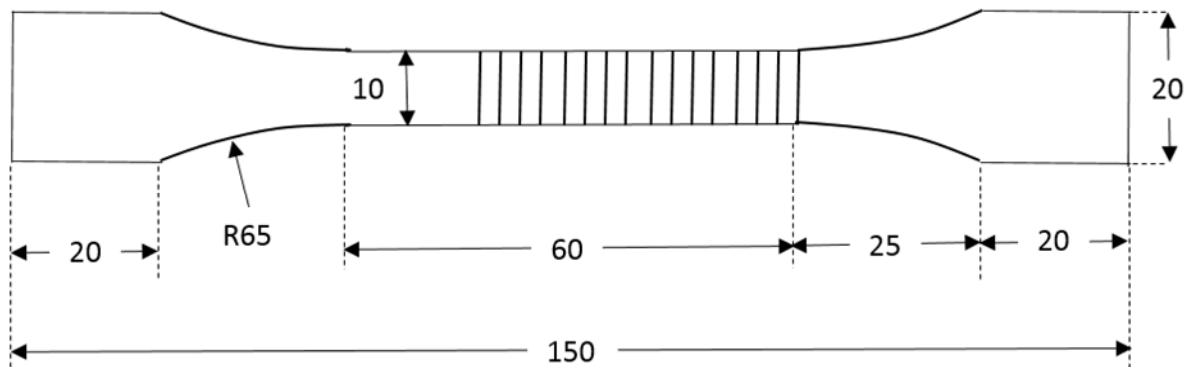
Geometrie des CFK-Probekörpers für den Querzugversuch, die Maße sind in mm angegeben. (115) (116)
